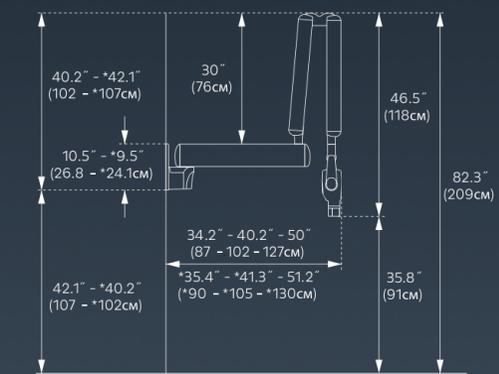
Представлены размеры для одинарного крепления и короткого конуса. *Обозначает размеры для крепления с двумя шпильками.
